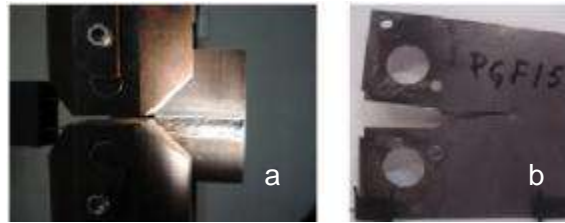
Imagen de una probeta compacta antes (con soldadura) y después (sin soldadura) de ser sometida al ensayo de fatiga, con un crecimiento de grieta de 23 mm
